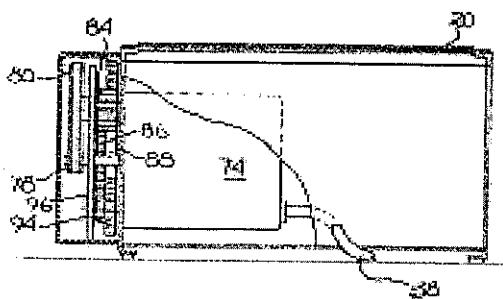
ลักษณะของเครื่อง Plastic Sheet Cleaning Machine
